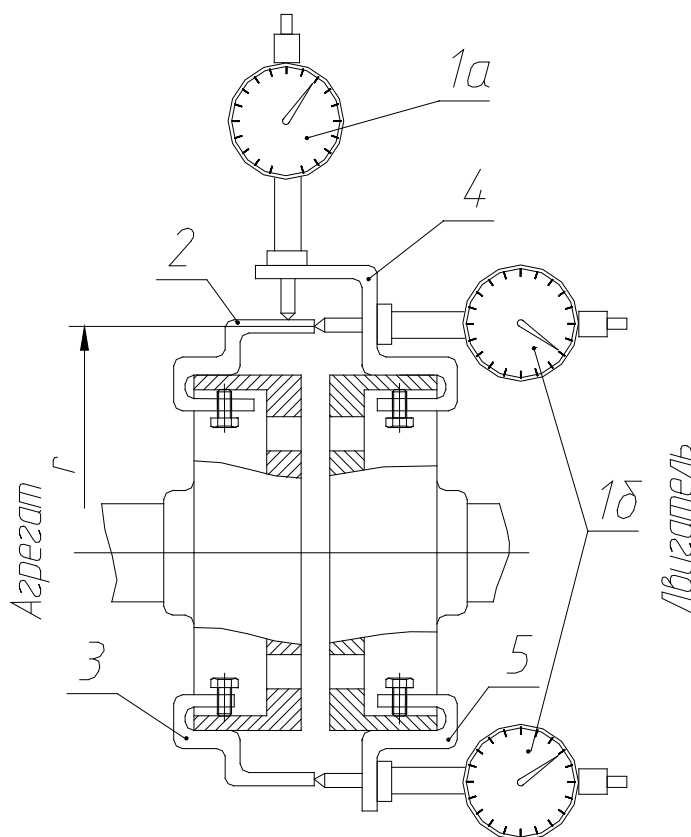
Приспособление для центровки, укрепленное на ободах полумуфт.
